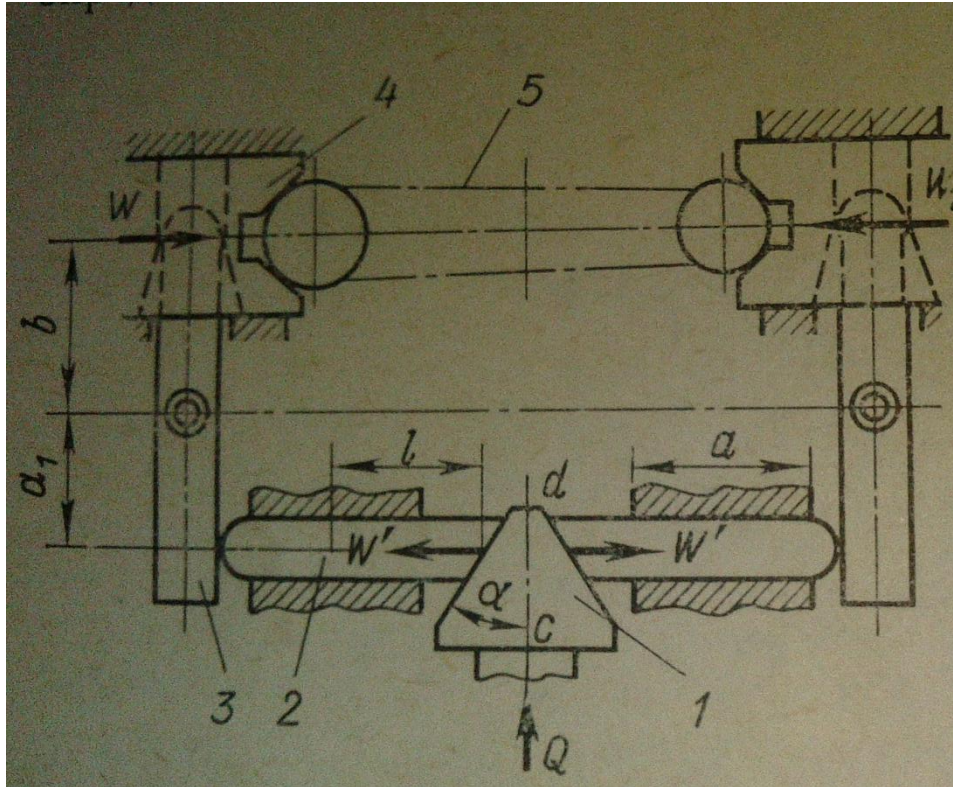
Схема комбінованого клиноплунжерного посилювача із клиноплунжерного та важельного механізма-посилувача для затиску деталі.
